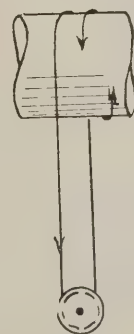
Selfaktorspindel mit Linksdrehung (Draufsicht)
